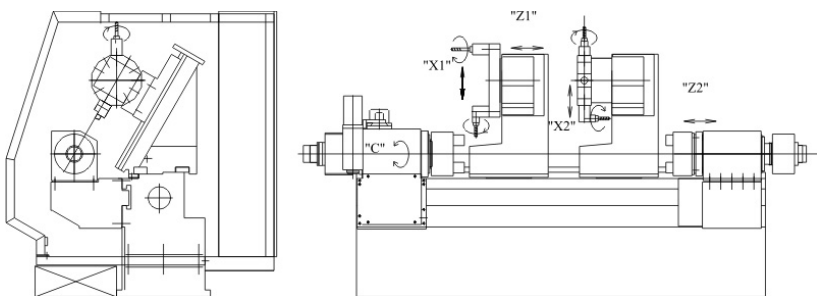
Центр токарный двухсуппортный с противошпинделем, с устройством позиционирования и круговой подачи шпинделя (осью С), револьверными головками для токарного и приводного инструмента на верхнем и нижнем суппортах
